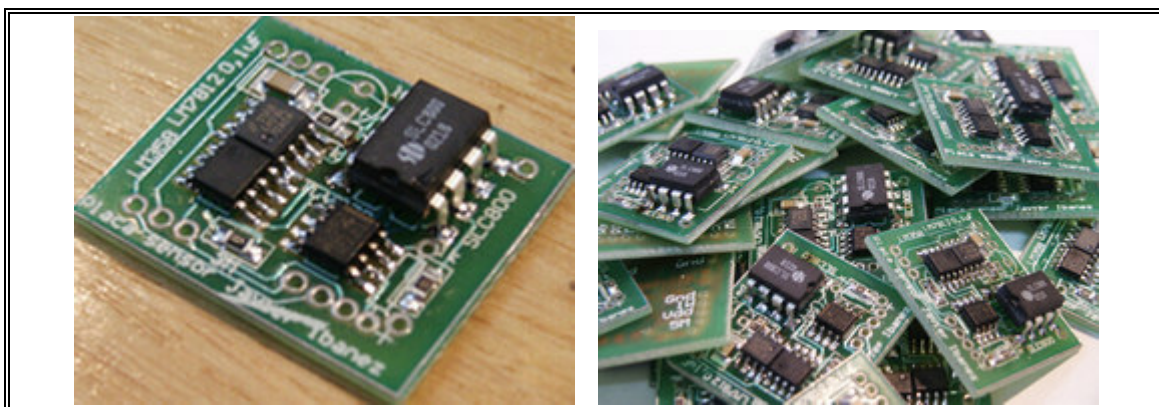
b) Dibujo tarjeta PCB de la arjeta de sensado
